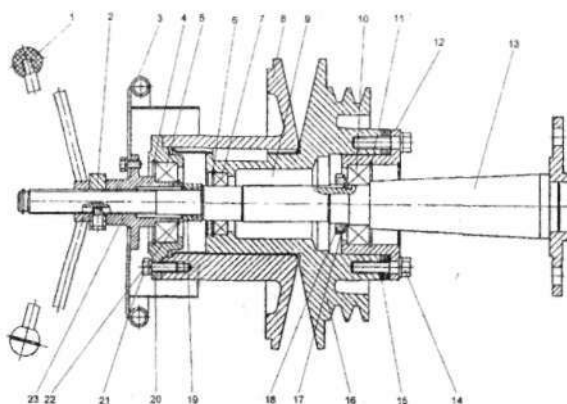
Регулировка вентилятора (контрпривод вариатора): 1 – ручка фиксатора; 2 – стопор; 3 – кожух; 4, 6, 11, 22 – кольца; 5, 7, 10 – подшипники; 8 – шкив подвижный; 9 – шпонка; 12 – стакан; 13 – ось; 14, 21 – болты; 15 – прокладки; 16 – шкив неподвижный; 17 – шайба; 18 – гайка; 19, 23 – втулки; 20 – корпус
